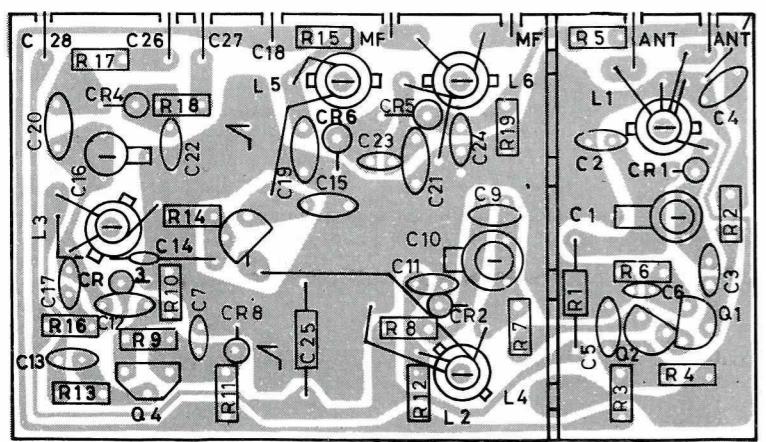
Plate FM-tuner, sett fra komponentssiden
